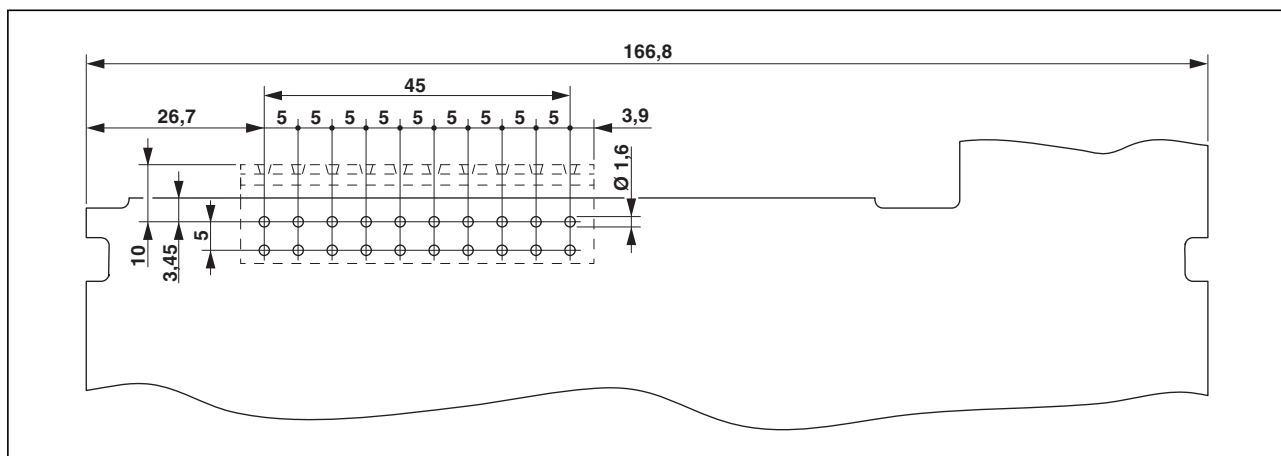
Maßzeichnung der Leiterplatte des Gehäuses bei Verwendung des Anschlusstechnik-Trägers CT20
